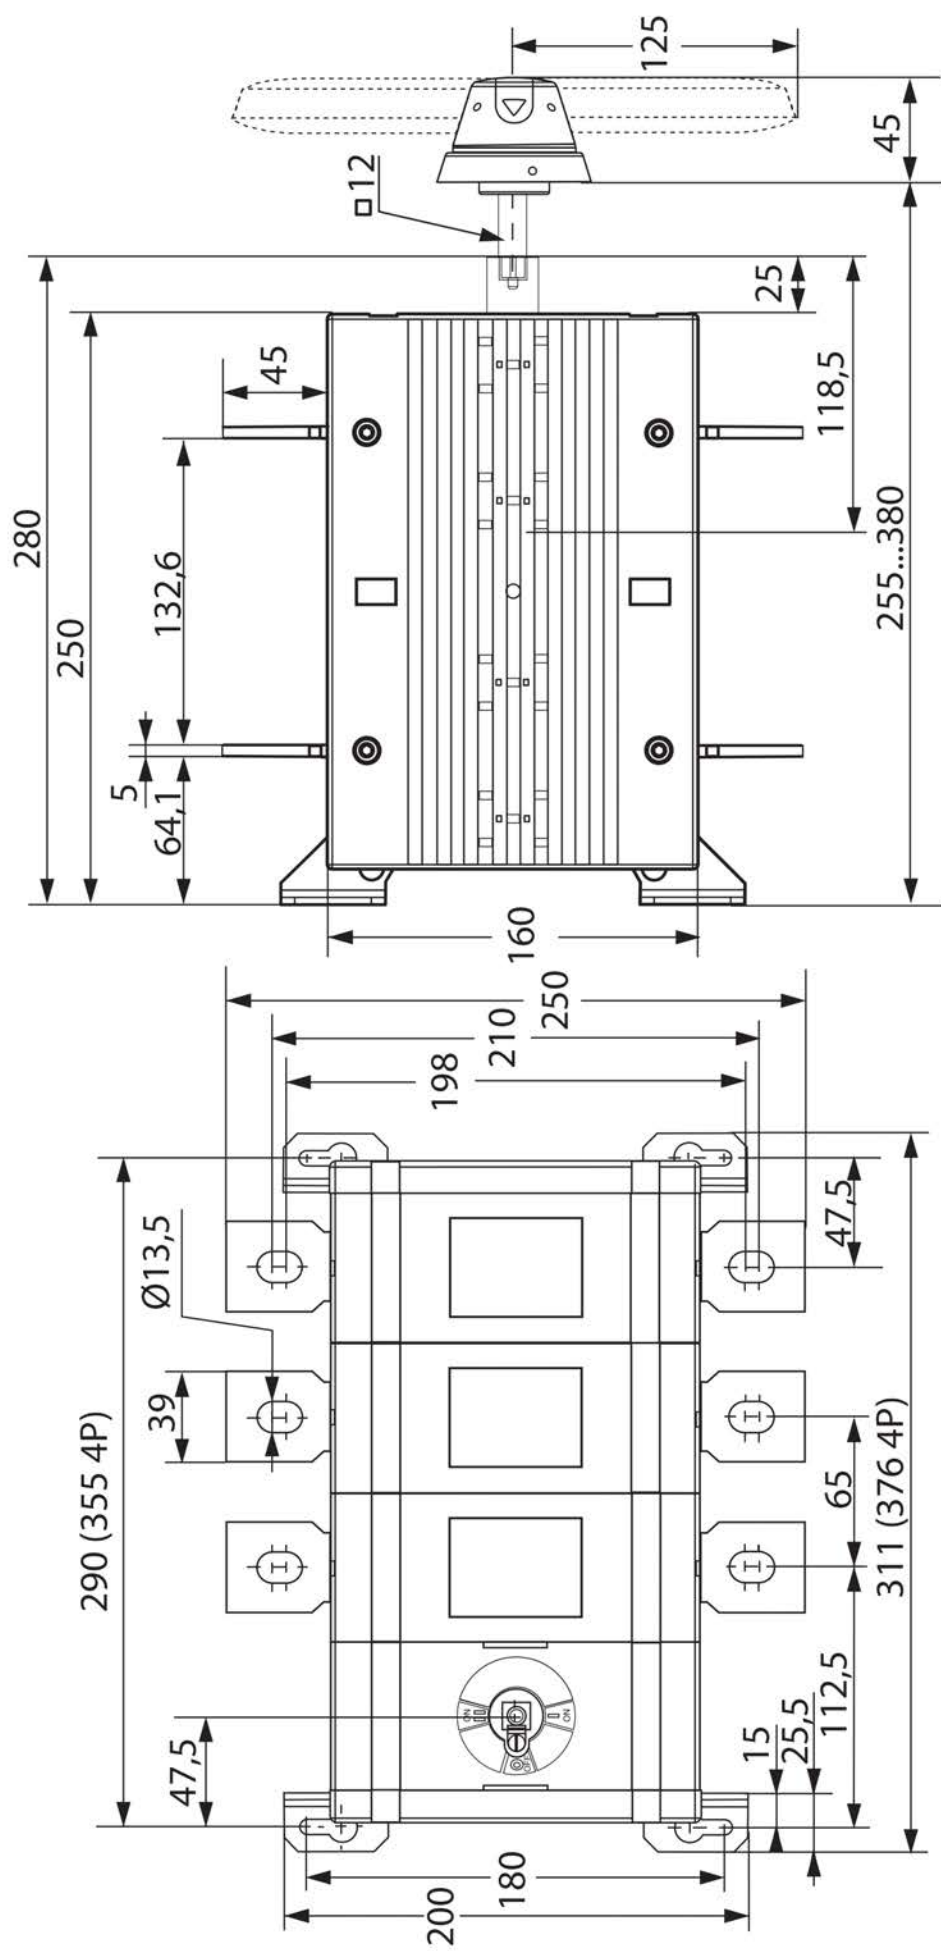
Габаритные и установочные размеры реверсивных рубильников 630-800 А
